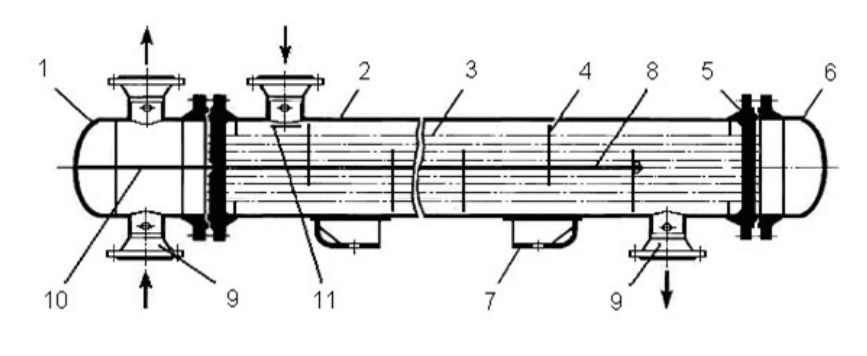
Кожухотрубчатый теплообменный аппарат с неподвижными трубными решетками
